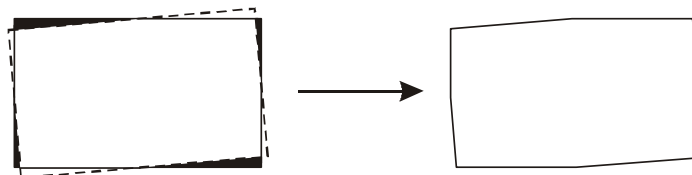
Схема образования дефекта переднего торца заготовки
